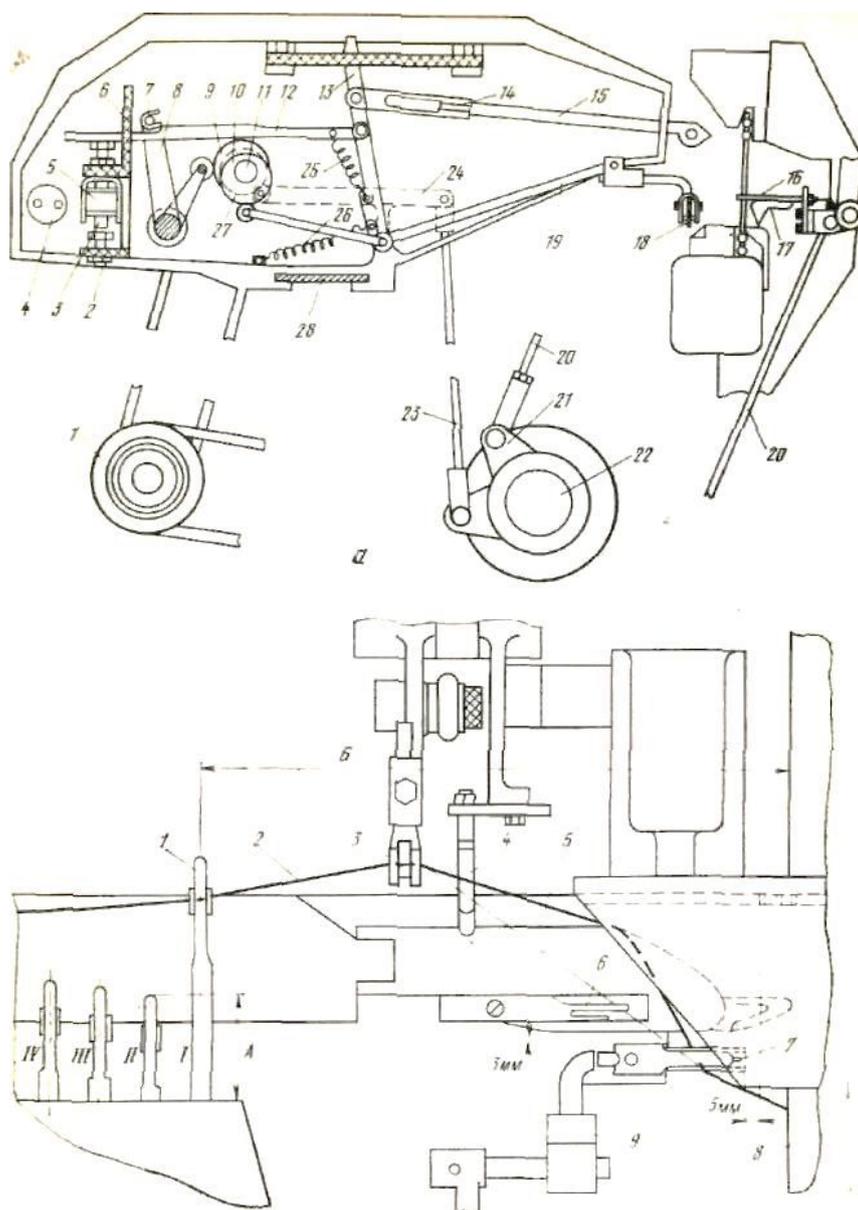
Механизм подачи утка к рапире: а - схема передачи движения нитенаправителем; б - схема передачи утка рапире.
